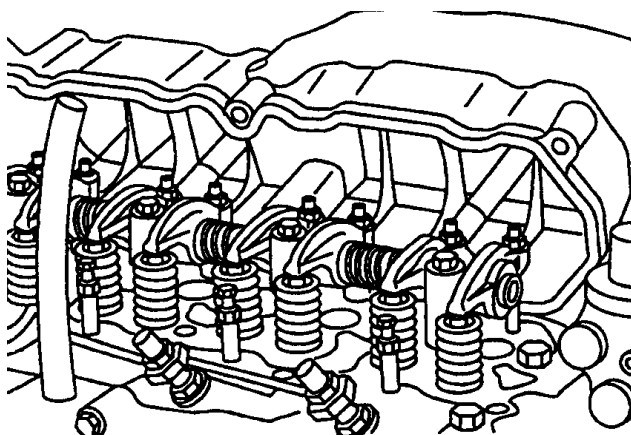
Демонтаж крышки головки блока цилиндров двигателя MITSUBISHI
